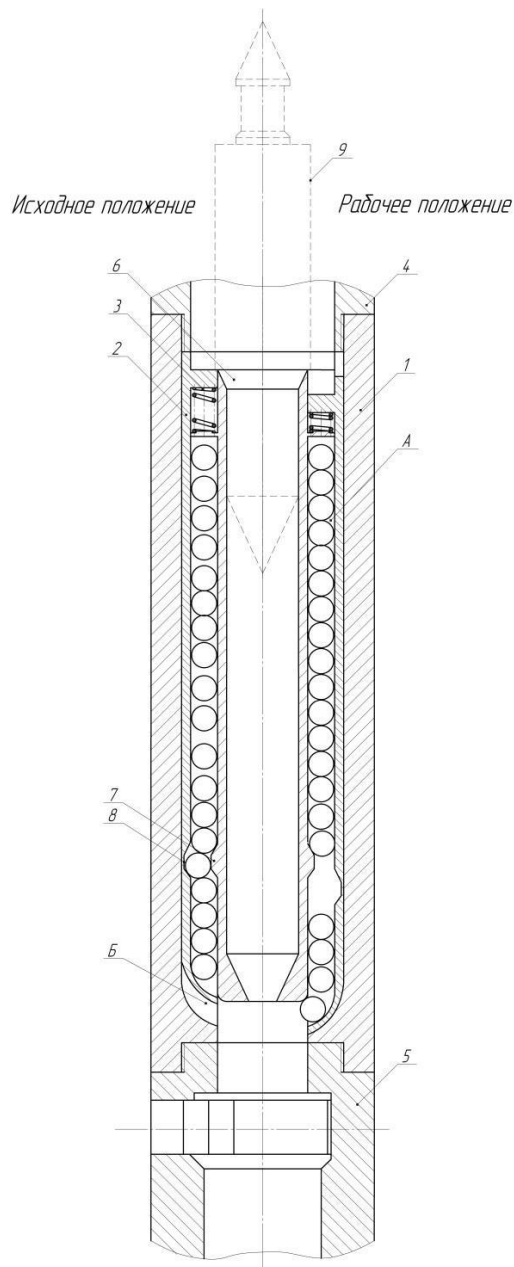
Комбинированный разрез забойного шаропитателя IV:
